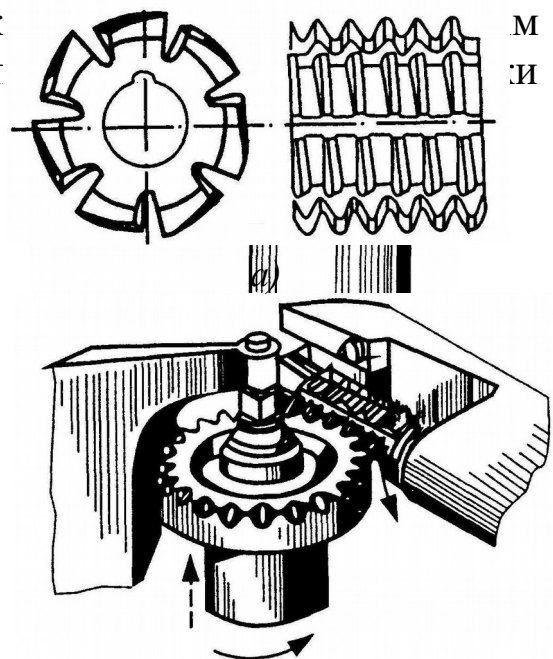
Нарізання зубчатих коліс черв'ячною фрезою
